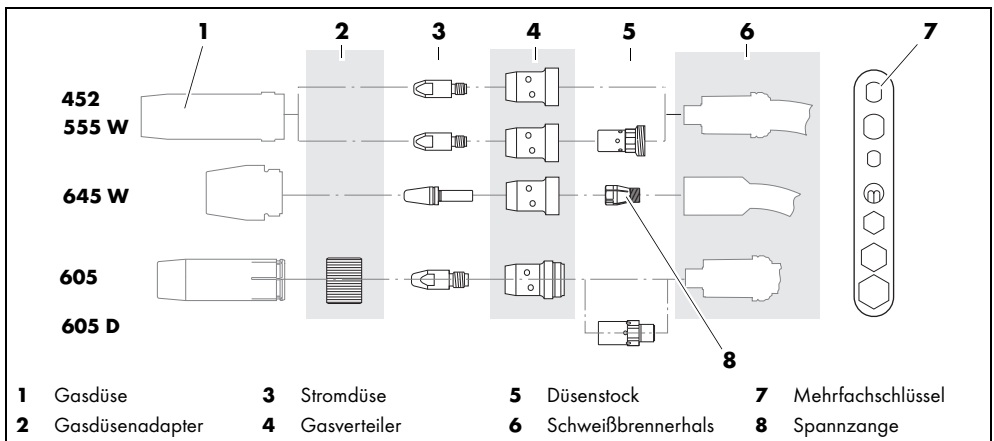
MT Schweißbrenner ausrüsten
